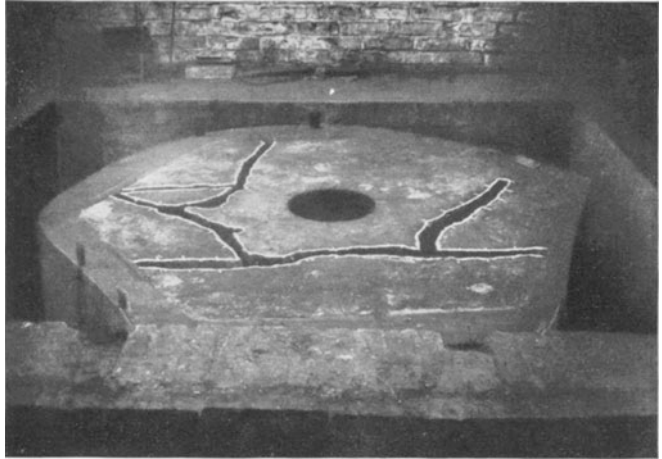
Zur Warmschweißung vorbereitete Ständerplatte.
